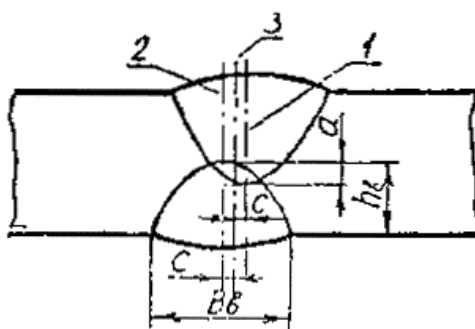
Схема определения геометрических параметров сварного шва по макрошлифу:
